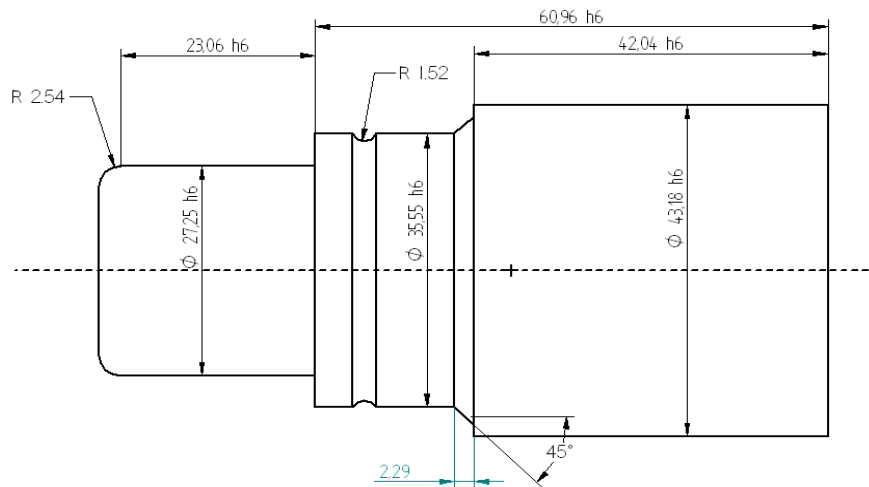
Dimensiones y tolerancias de la pieza de revolución.
